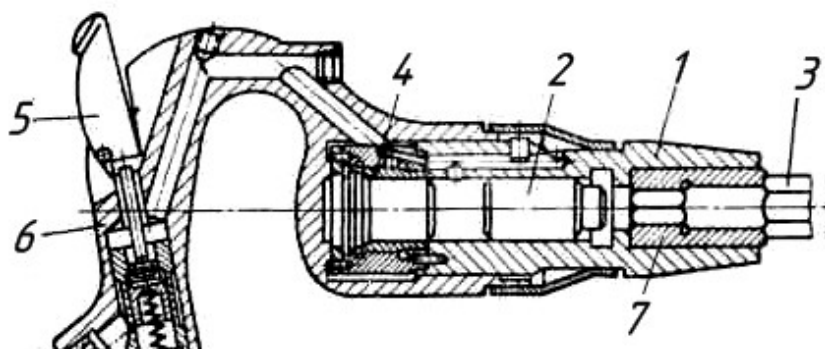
Пневматический рубильный молоток для обрубki чугунных отливок: 1 – ствол; 2 – ударник; 3 – хвостовик зубила; 4 – золотник; 5 – курок; 6 – рукоятка; 7 – букса
